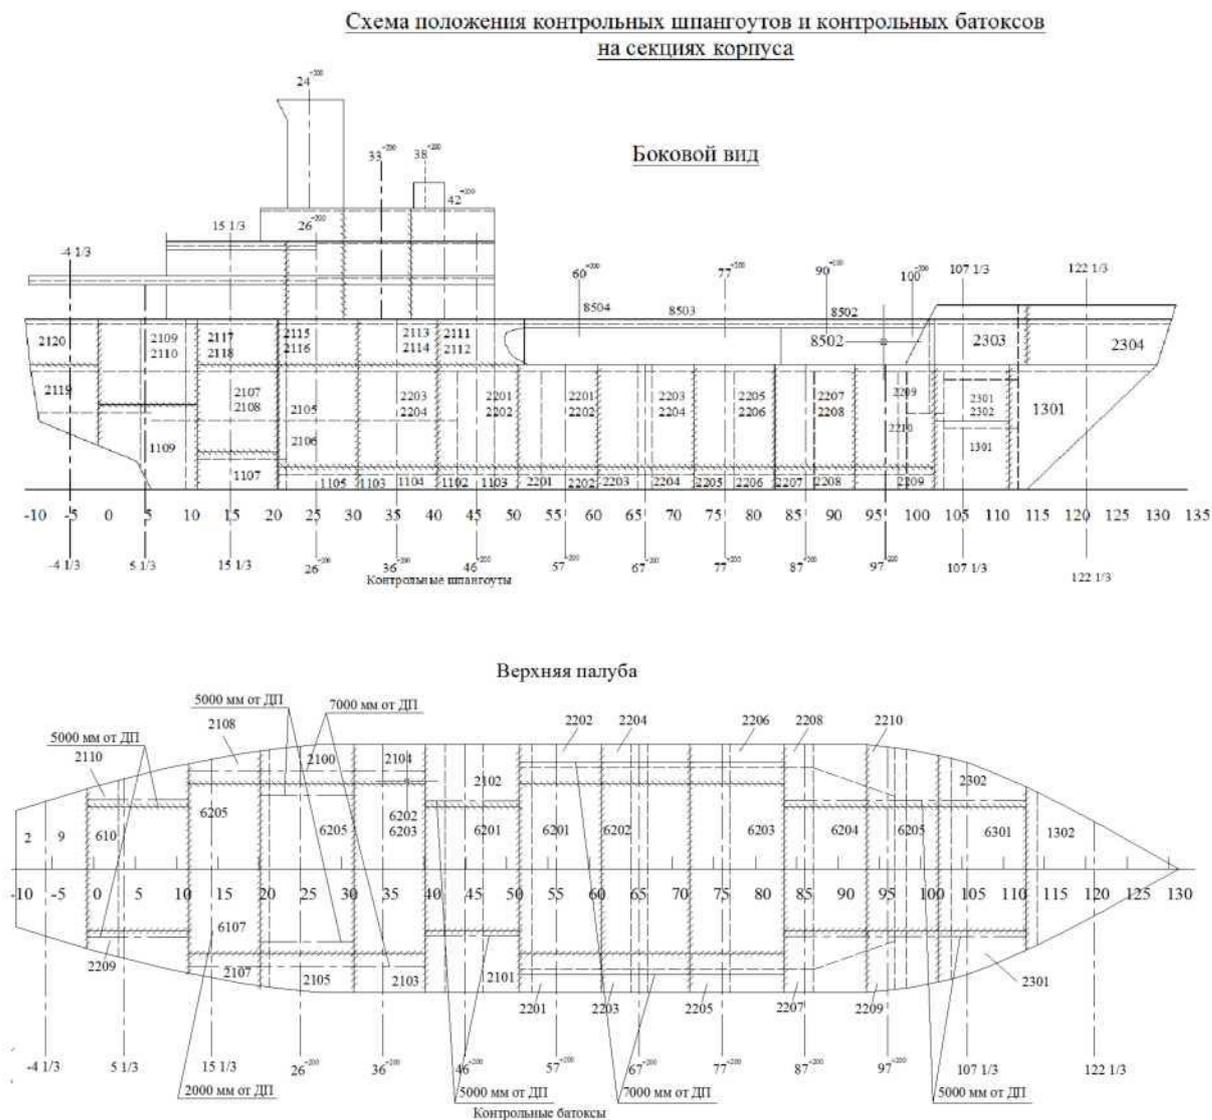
Пример выполнения чертежа разбивки корпуса на сборочные единицы
